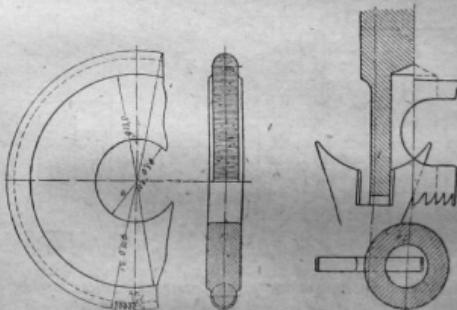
Полуавтомат Джик и Хазлер для фрезеровки пазов анкера.
